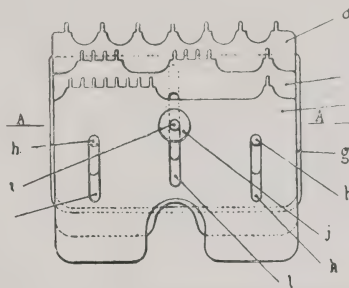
Zusammengesetztes Werkzeug für mehrere Muster
